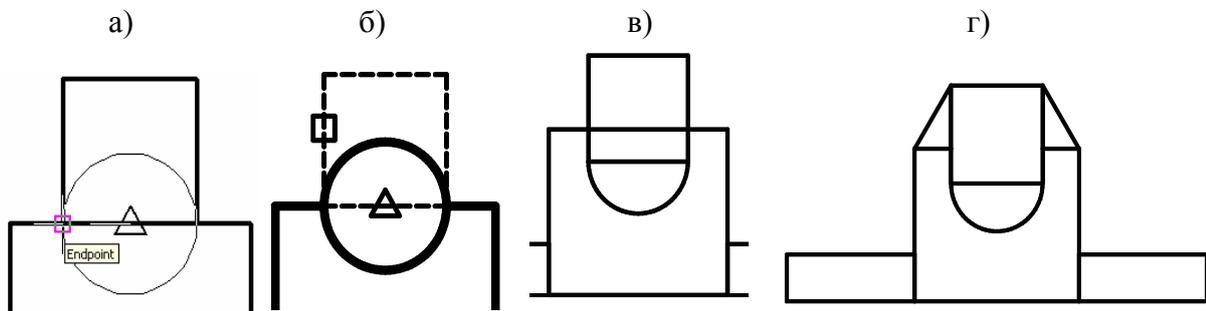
Разработка схемы вертикально-сверлильного станка CBA:
